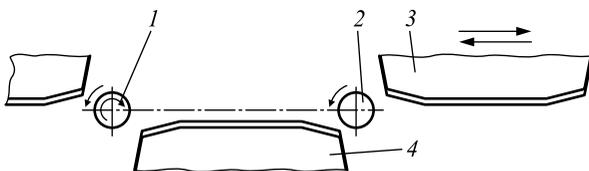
Схема накатывания резьбы плоскими плашками:
